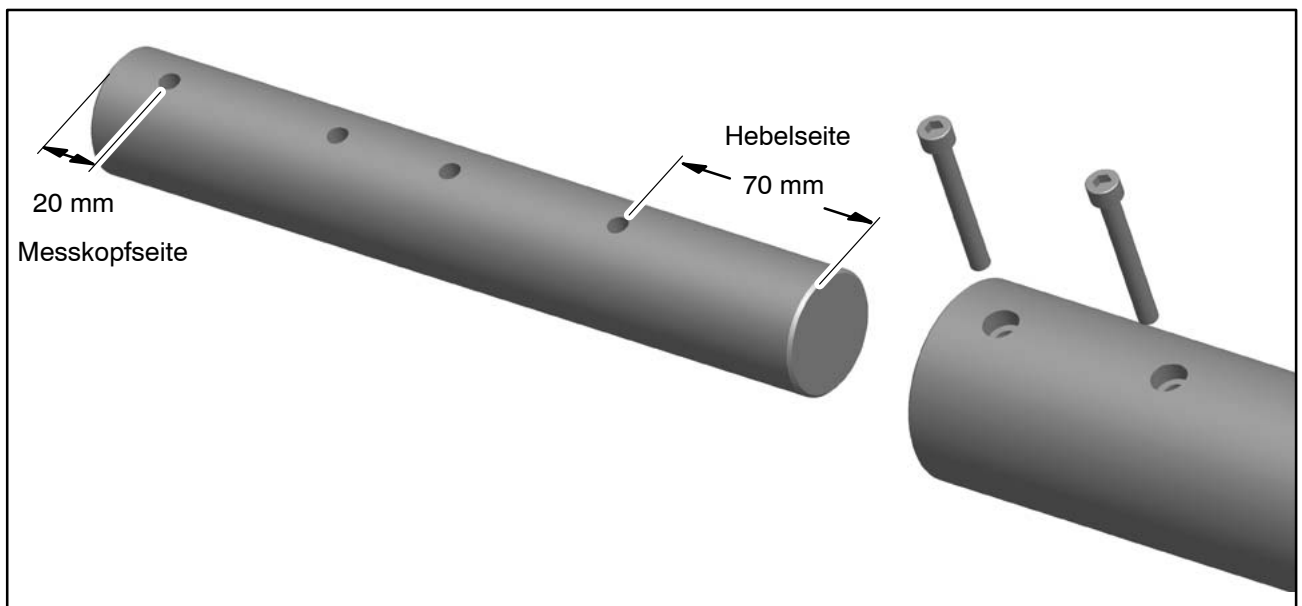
Seitenorientierung des Verbindungsbolzens, Detailansicht
